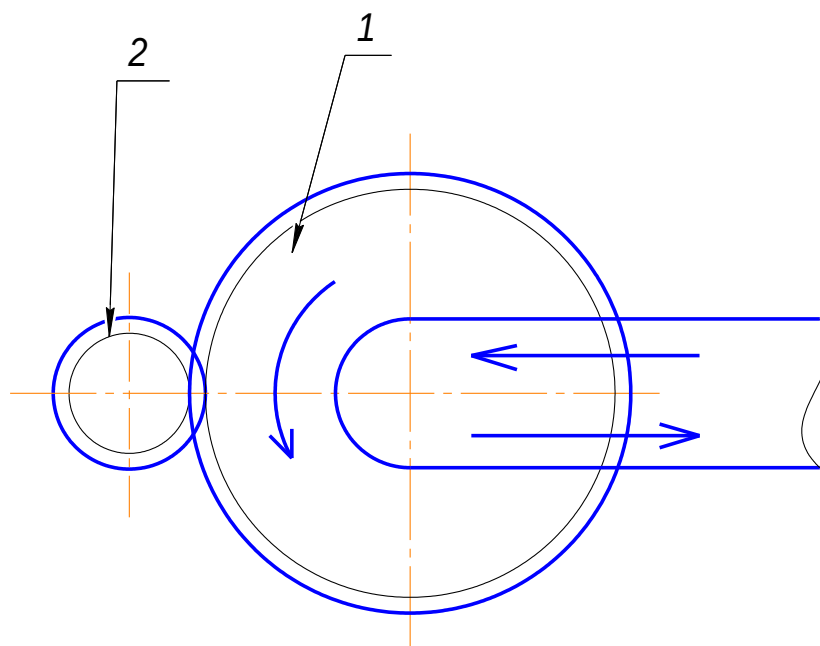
Накатывание с радиальной подачей одним роликом с винтовой нарезкой: 1 – вращающийся ролик; 2 – обрабатываемая деталь
